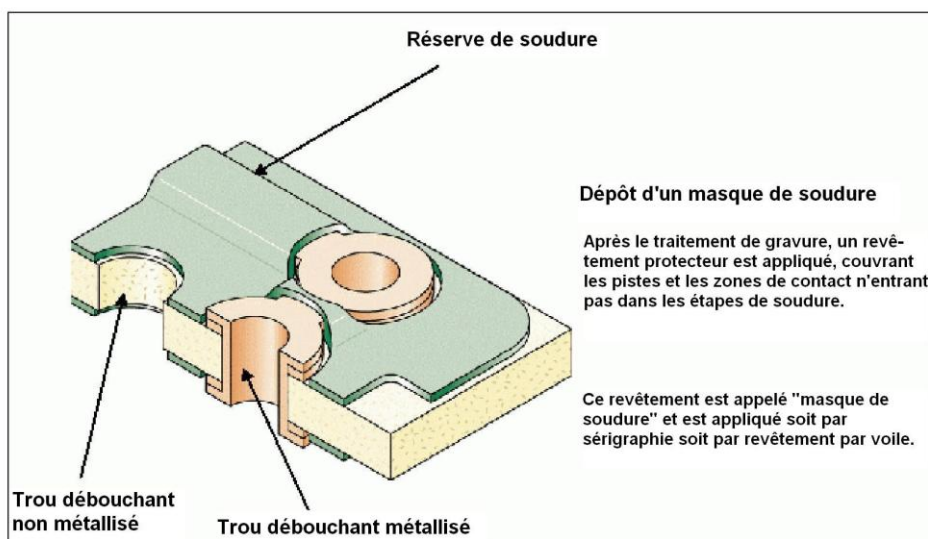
Revêtement d'un masque de soudure
